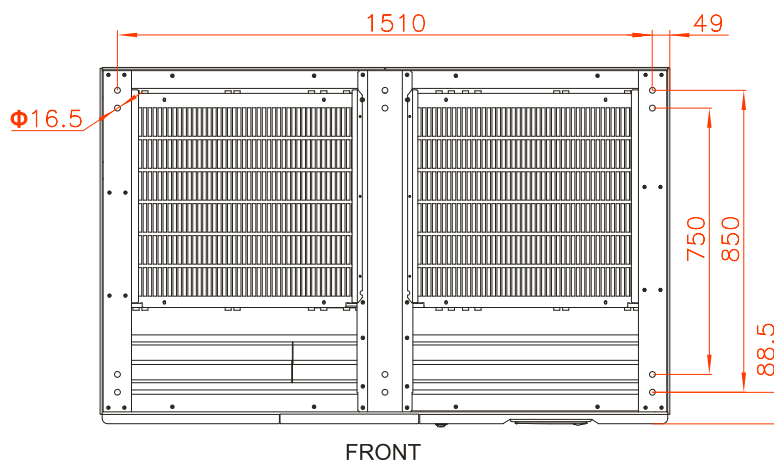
Монтажная рама с размерами для FR-UK(/B)33(300-400) (вид сверху)
